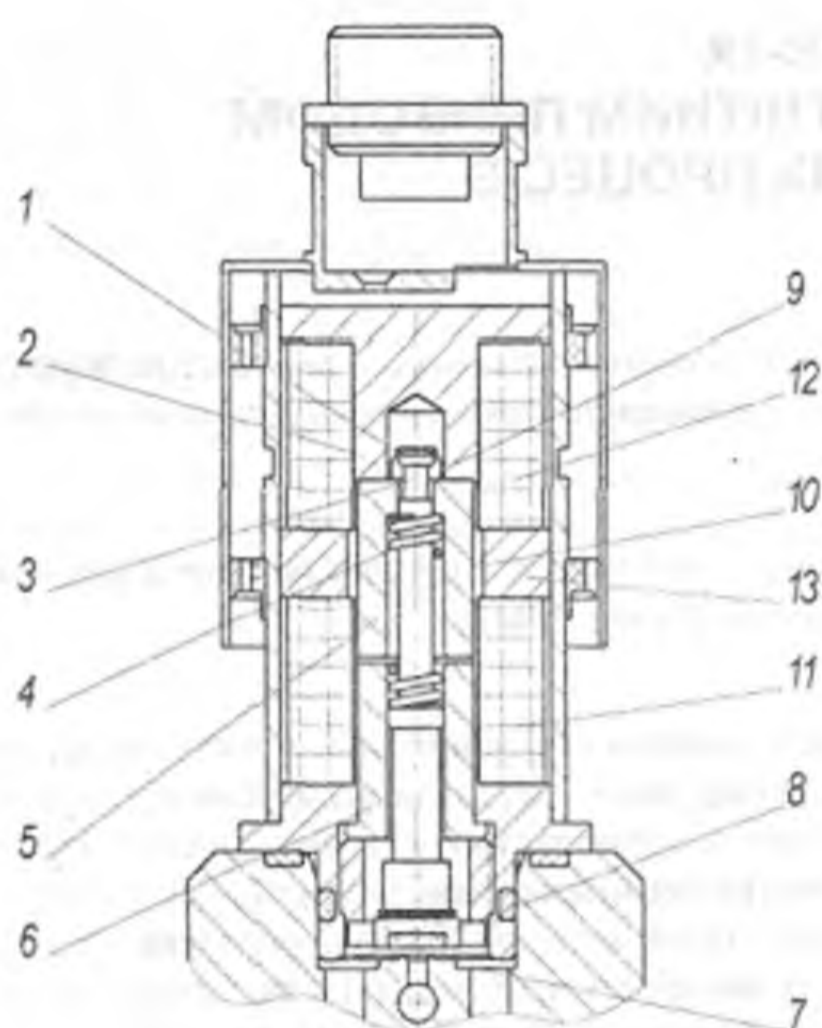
Конструктивна схема клапана з двопозиційним електромагнітним приводом: 1 – головка штока; 2 – корпус електромагніта; 3 – шийка штока; 4 – буферна пружина; 5 – повзун (якір); 6 – нижній стоп; 7 – сідло; 8 – золотник; 9 – стопорна шайба; 10 – трубка розподільна; 11 – обмотка закриття; 12 – обмотка відкриття; 13 – постійний магніт.
